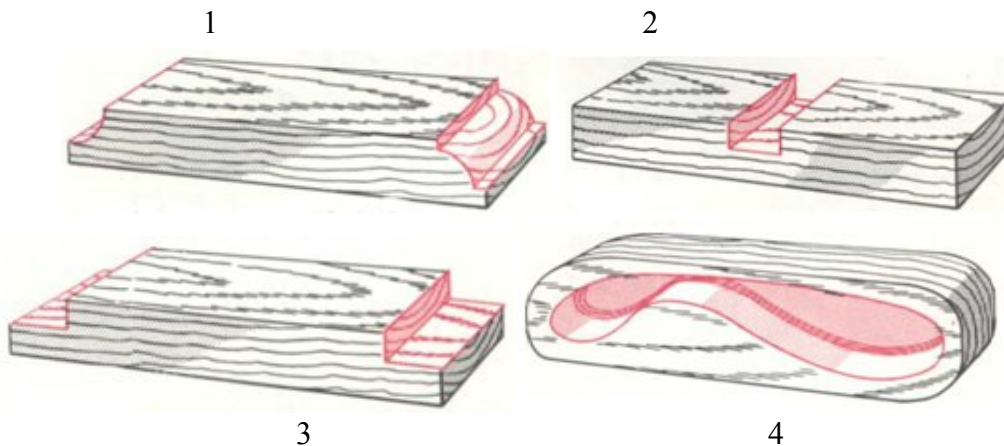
Види робіт що виконуються на фрезерних верстатах
